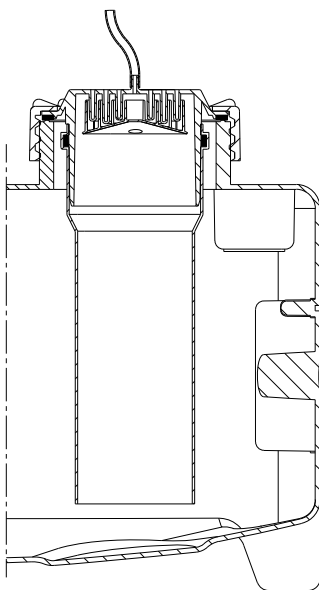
Крышка с резьбой и пневматическая трубка, трубка DN 100 и уловитель конденсата
